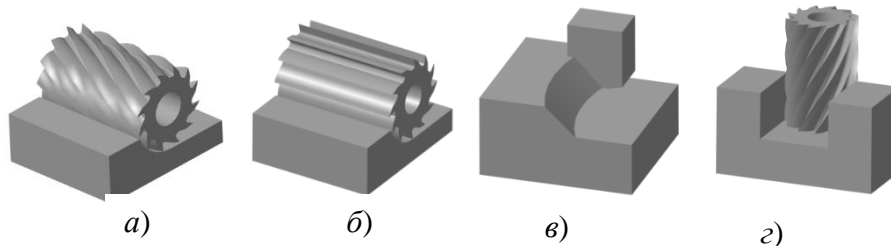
Схеми різання та умови контакту при фрезеруванні
